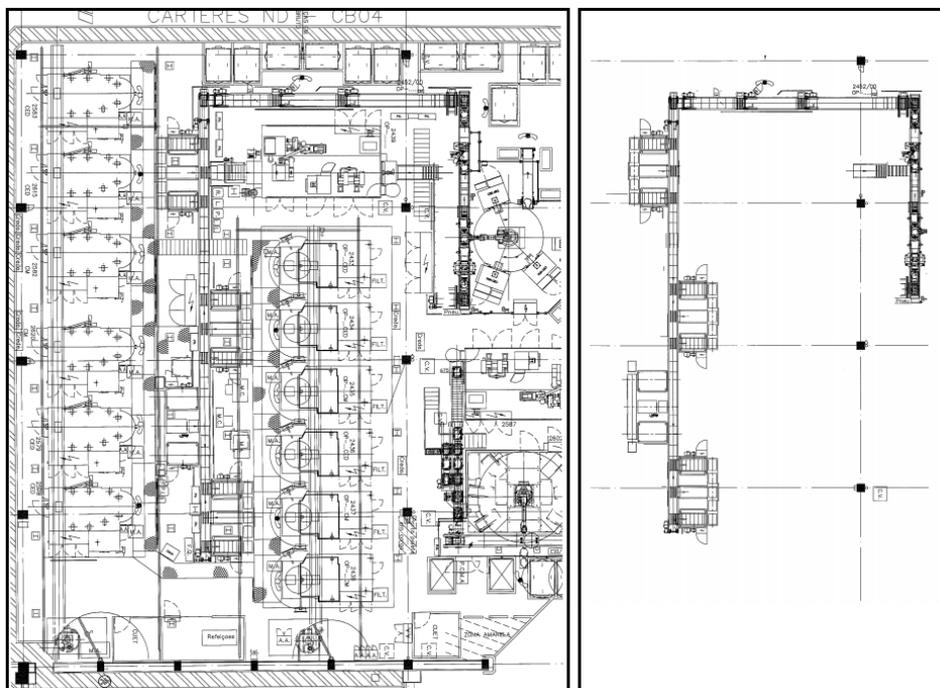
Layout e planta do transportador do módulo 1 (À esq.: layout módulo 1; À dir.: transportador módulo 1)
